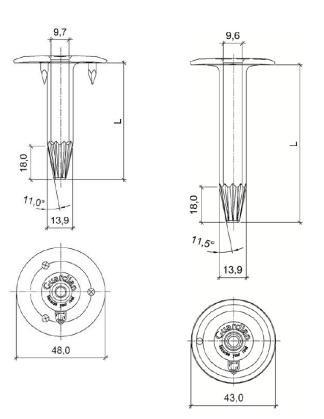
Plaquette de fixation Fig. 9— Plaquette de fixation GUARDIAN RB 48 GUARDIAN R 45
